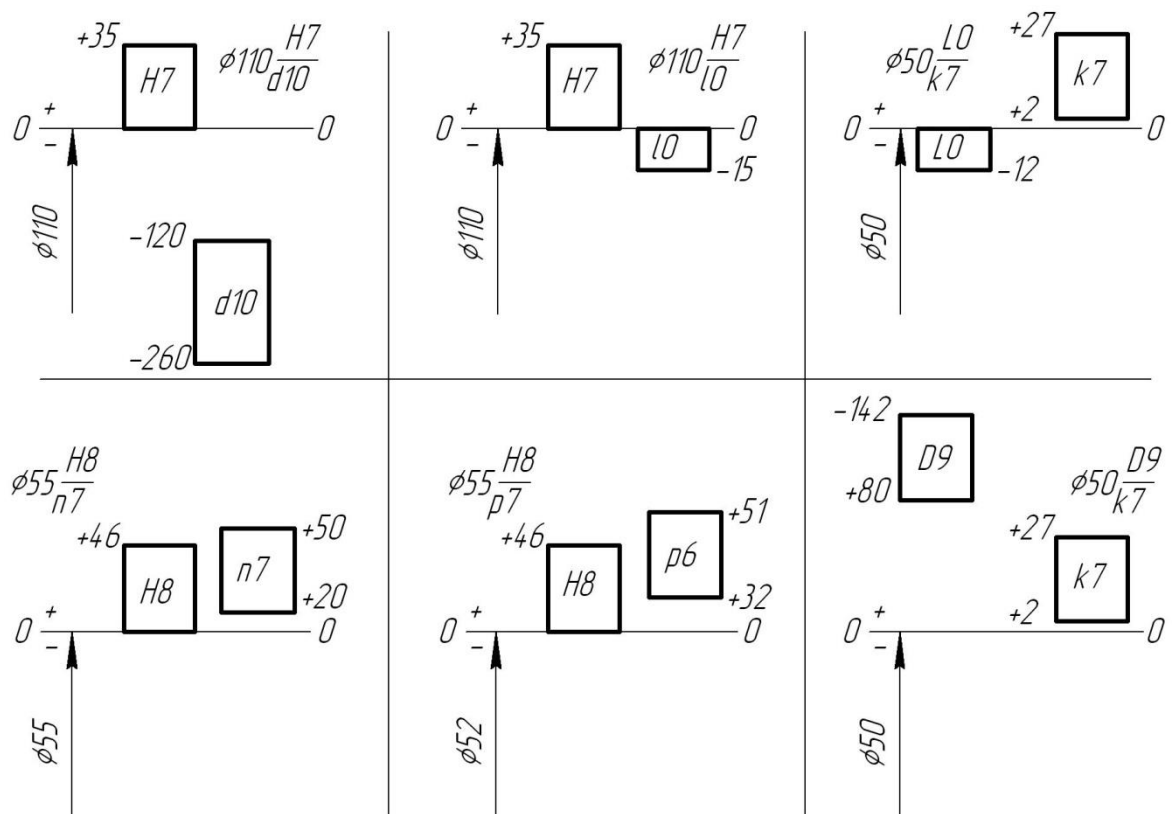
Схема расположения полей допусков посадок промежуточного вала редуктора
